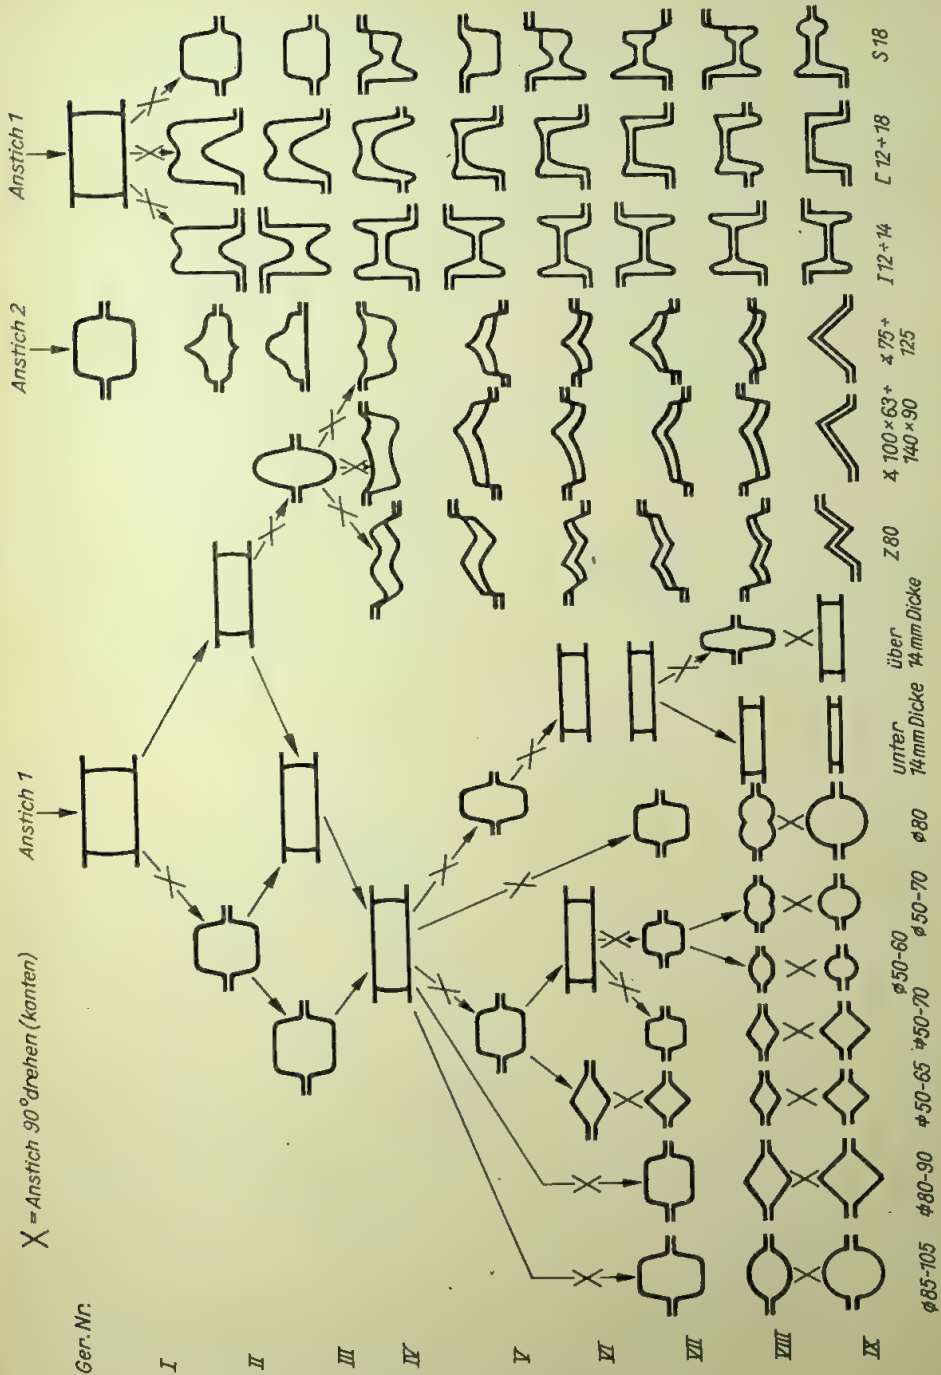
Kalibrierung und Walzplan einer Mittelstraße für Profile
